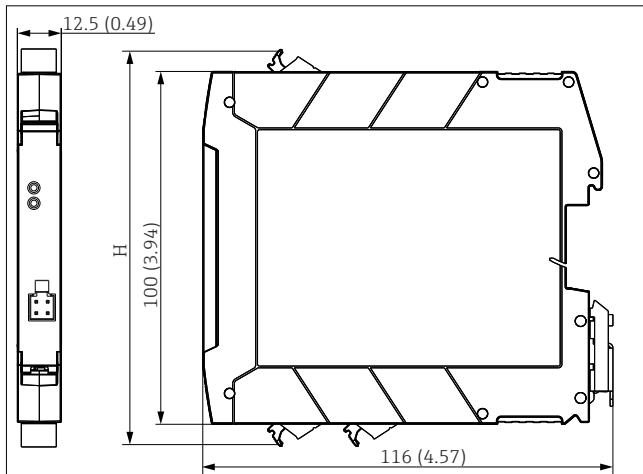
Dimensioni del trasmettitore per guida DIN Dimensioni in mm (in)
